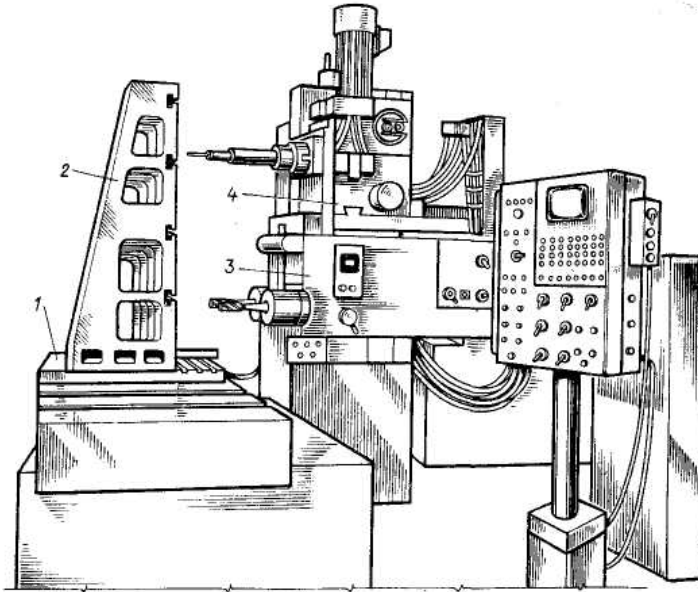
Внешний вид копировально-фрезерного станка мод. ЛР397ФЗ: 1 – стол; 2 – стойка; 3 – шпиндельная бабка; 4 – трехкоординатное измерительно-управляющее устройство
